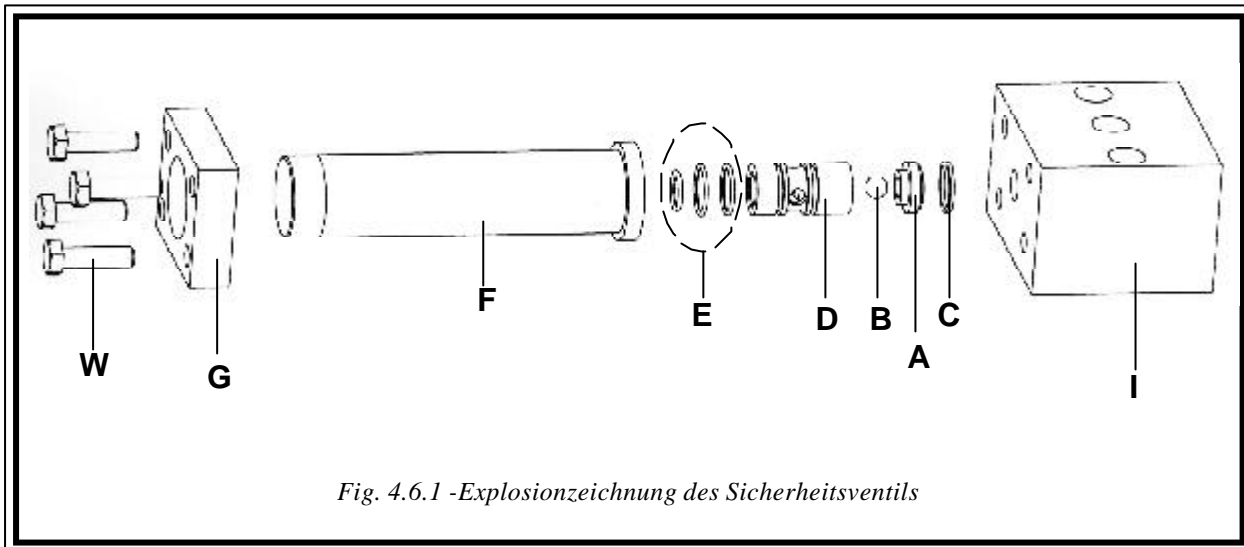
Explosionzeichnung des Sicherheitsventils
